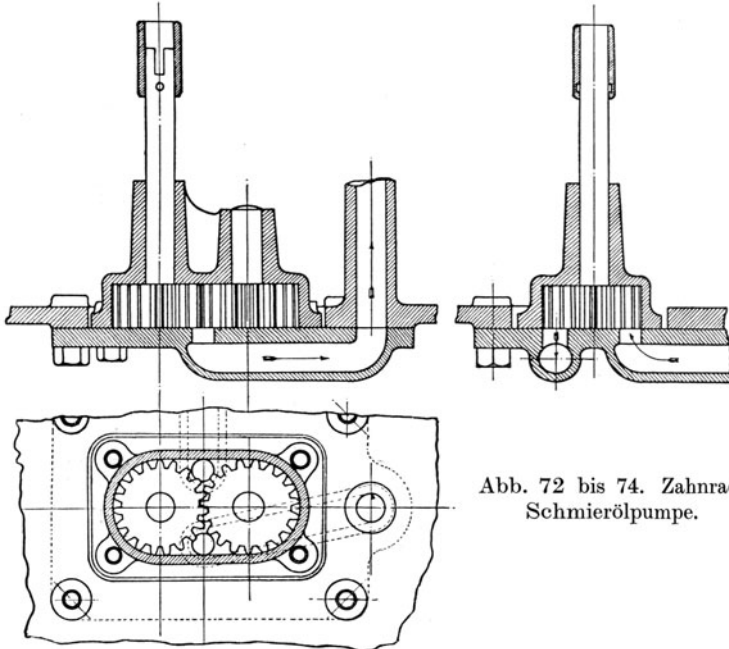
bis 74. Zahnrad-Schmierölpumpe.
